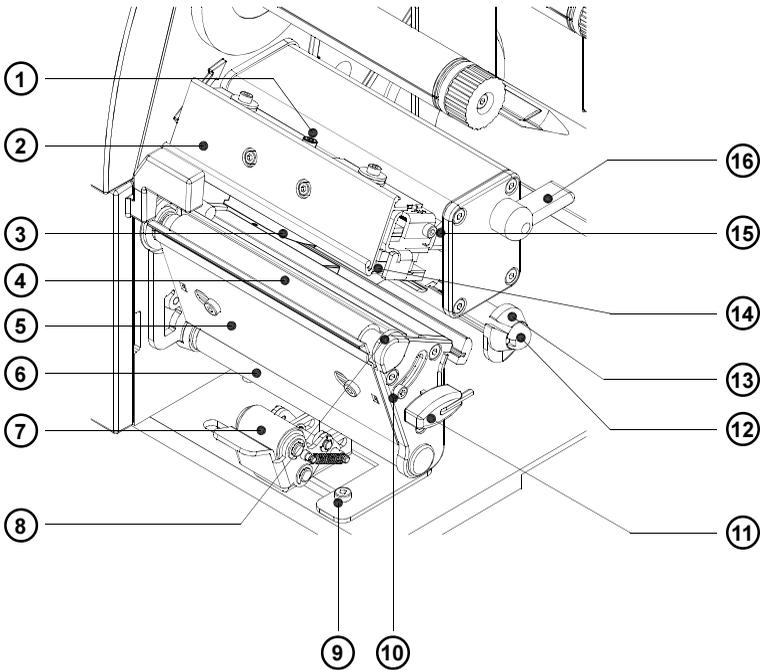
Druckmechanik A2/200P Gemini bei geöffnetem Druckkopf
